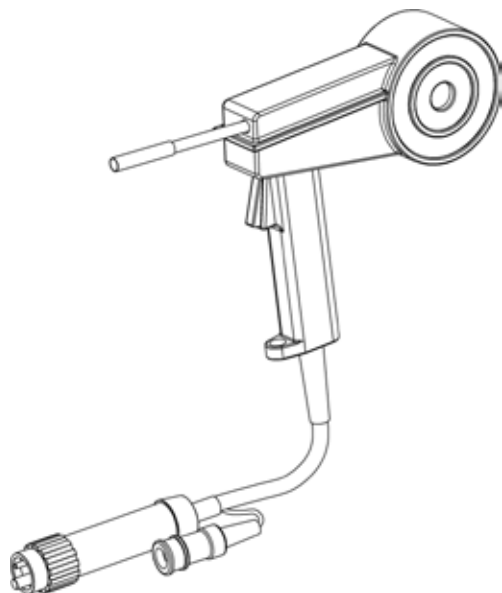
Горелка для MIG сварки типа «Spool gun».
